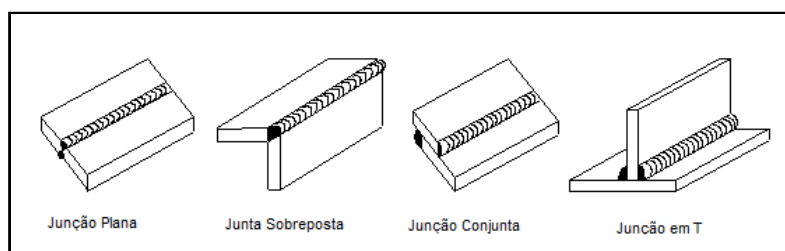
Tipos de junta na soldagem com eletrodo revestido
